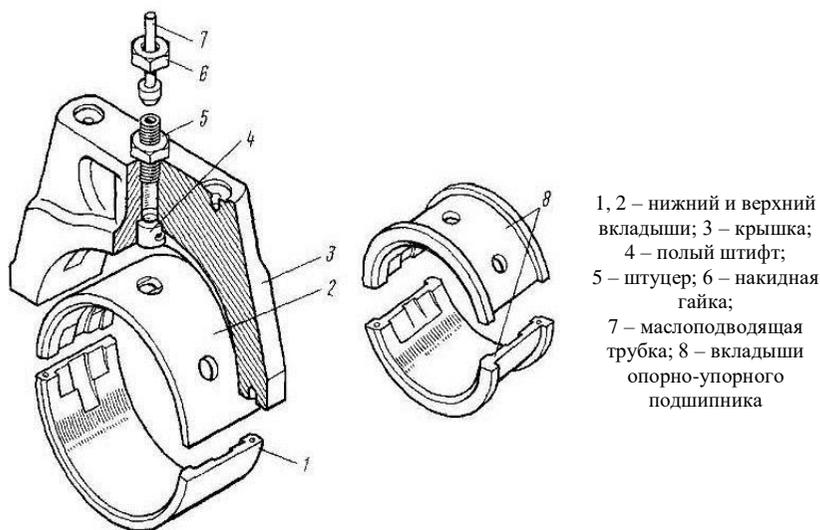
Коренные подшипники коленчатого вала дизеля ПД1М
